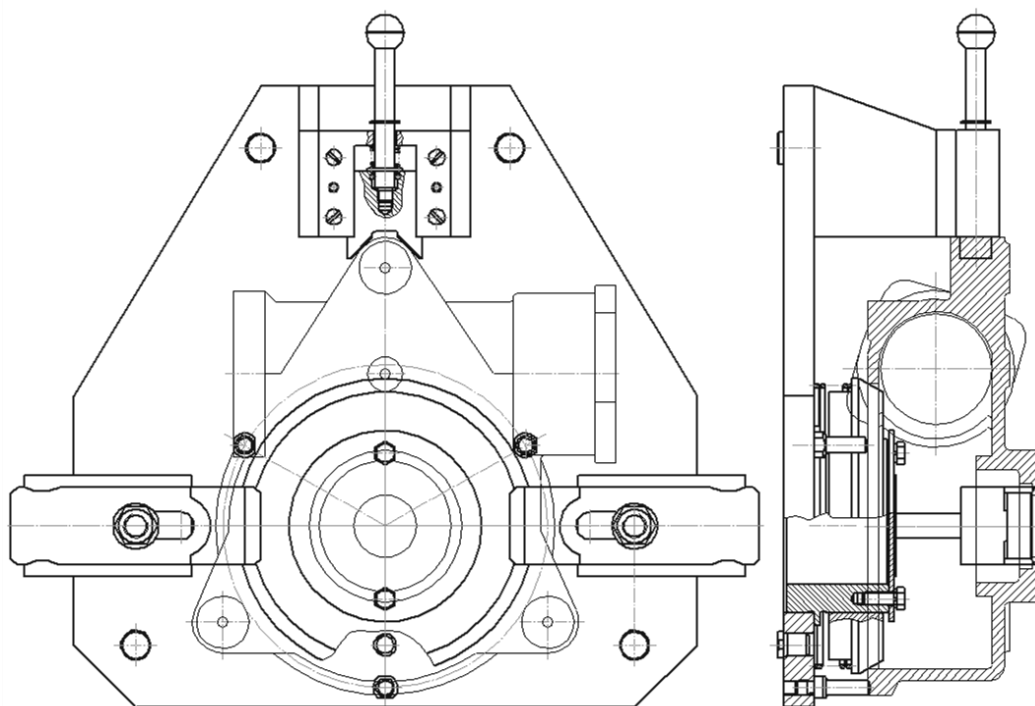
Схема установки детали «Корпус промежуточный» на операции 005
